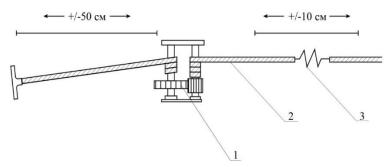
Схематичное изображение передаточного механизма без корпуса
